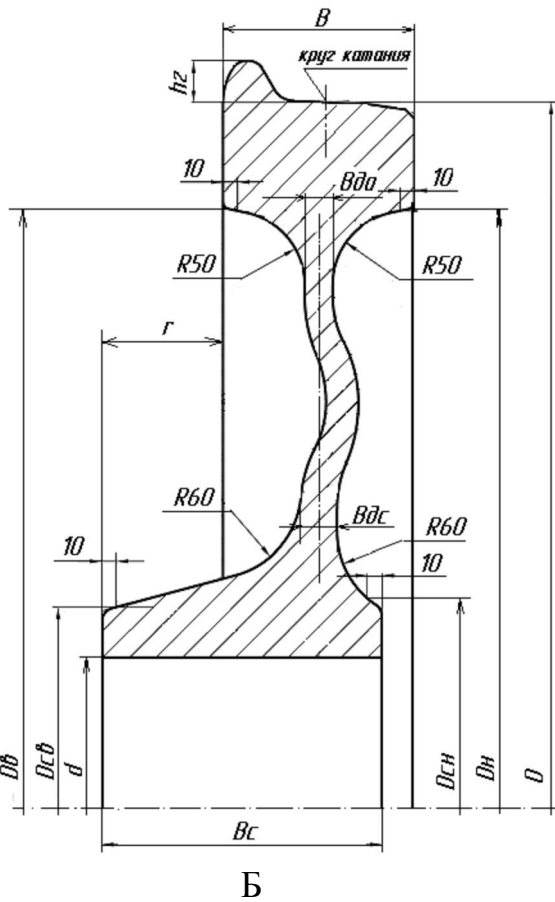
Конструкция и основные размеры колеса цельнокатаного
